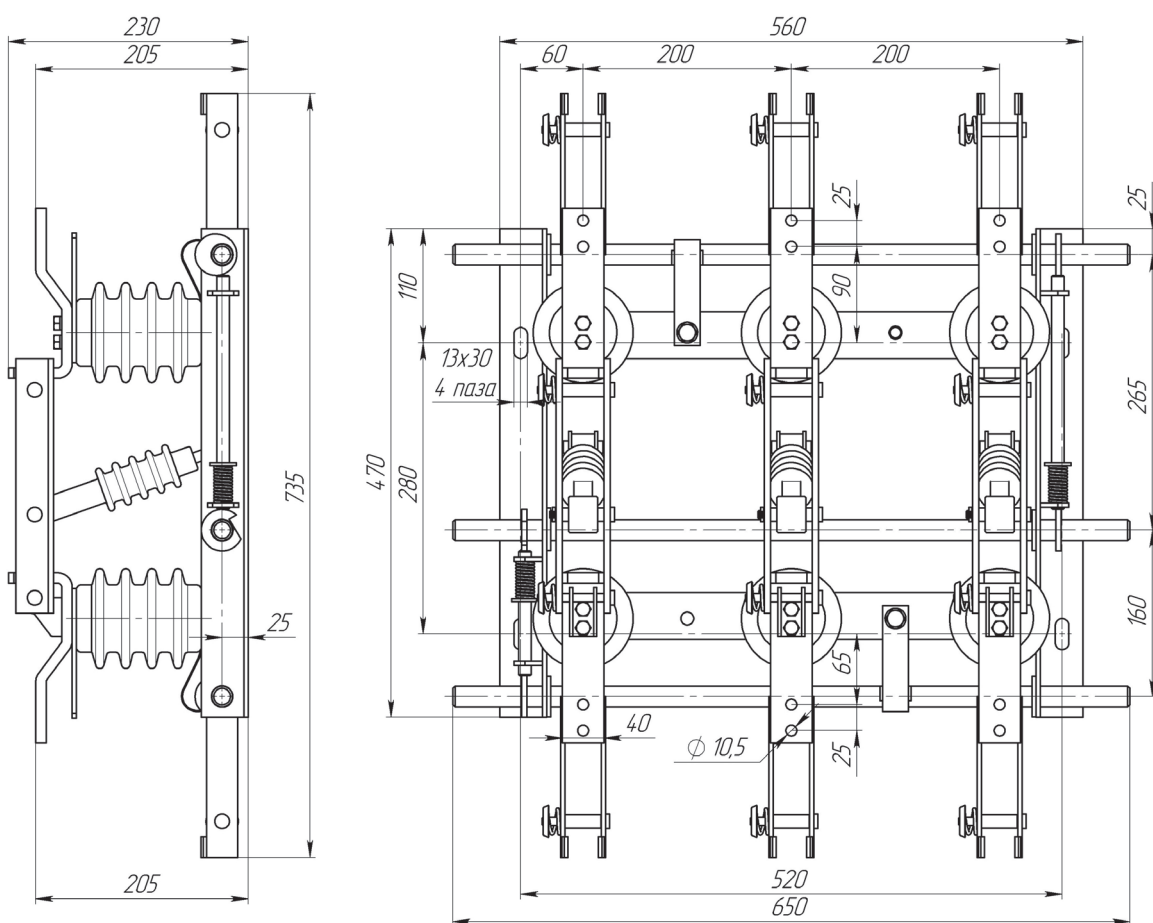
Габаритные и установочные размеры разъединителя РВз-III 10/1000 УХЛ12
